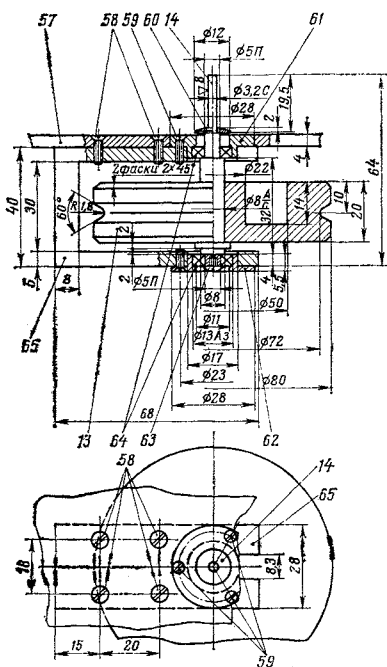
Узел ведущего вала: 13 — маховик, ЛС59-1, напрессовать на дет. 14; 14 — ведущий вал, Ст. ХВГ, калий НРС58...60; 57 — панель ЛПМ, Д16А-Т; 58 — винты М3×10, 4 шт.; 59 — винты М2,5×10, 6 шт.; 60 — шайба защитная, фторопласт (органическое стекло); 61, 62 — корпус шариковых подшипников, ЛС59-1; 63 — винт М2, 5×3; 64 — шариковые подшипники 1000095 (5×13×4 мм), 2 шт.; 65 — кронштейн, Ст.3.
